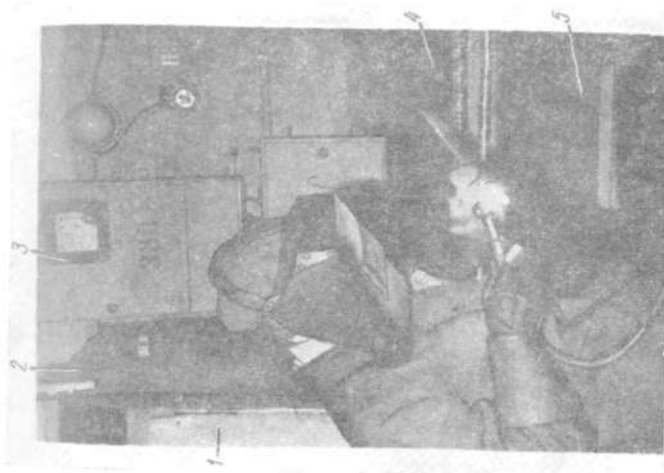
Рабочее место для сварки изделий на столе.
